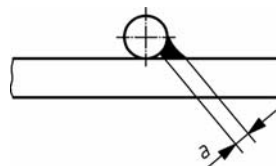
zeigt ein Beispiel für einen Überlappstoß. Die Bilder 2 und 3 zeigen Beispiele für Kreuzungsstöße. Die Länge der Schweißnaht, l , und die Kehlnahtdicke, a , sind von der Anwendung abhängig und müssen der WPS entsprechen.
